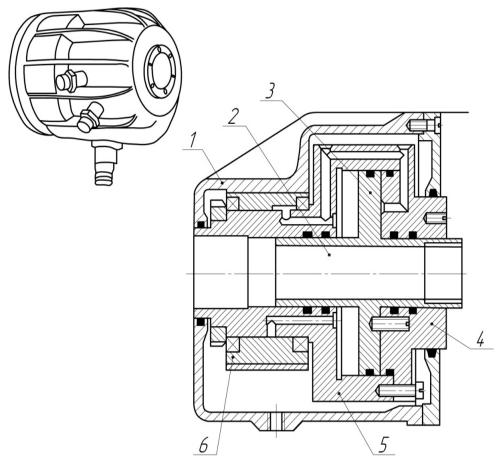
Гидравлический вращающийся цилиндр: 1 – кожух; 2 – шток; 3 – поршень; 4 – фланец; 5 – корпус; 6 – гидравлическая муфта
